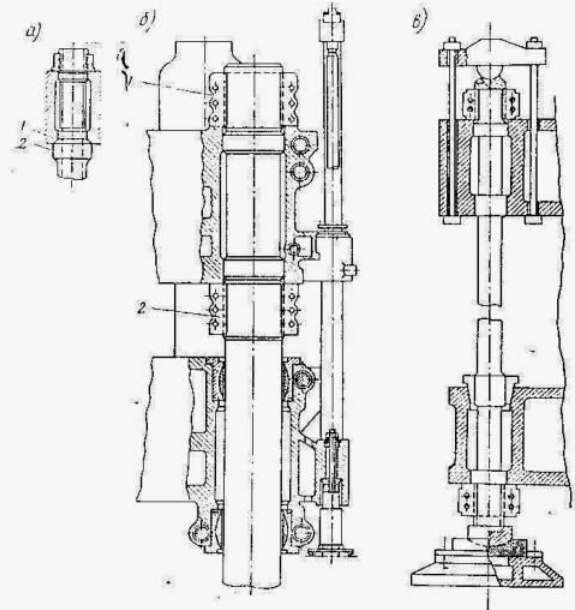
Схема закрепления колонн: а — колонны с буртами; б — колонны без буртов; в — колонны с опорой на фундамент и подвижной верхней поперечной
